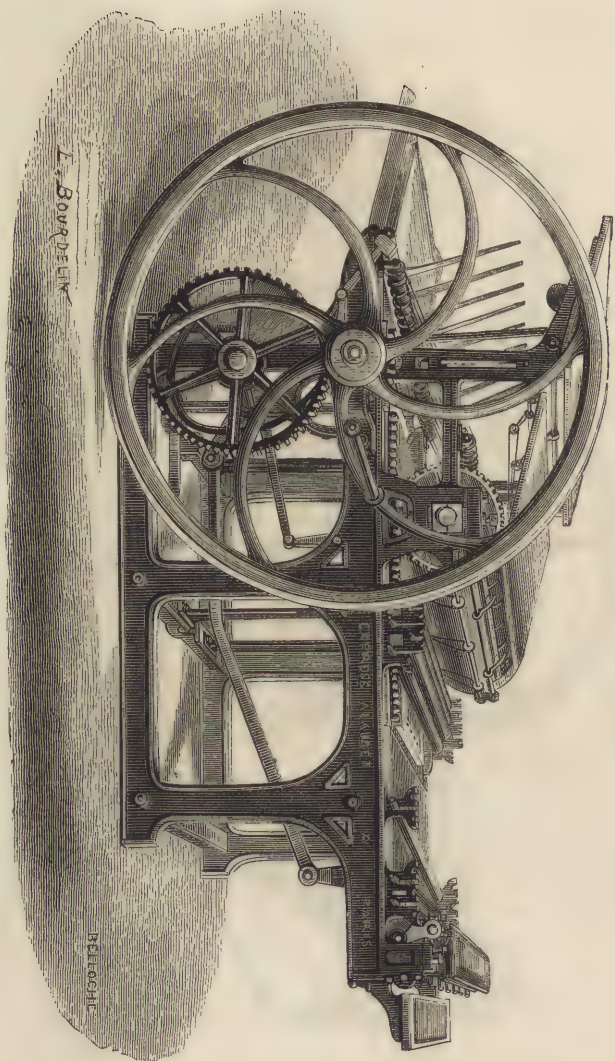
MACHINE EN BLANC, DITE « EXPRESS » (SYSTEME ALAUZET).
